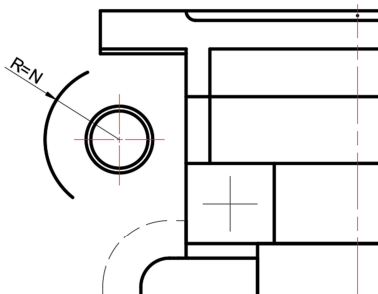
Часть окружности для формирования выступающей бобышки
